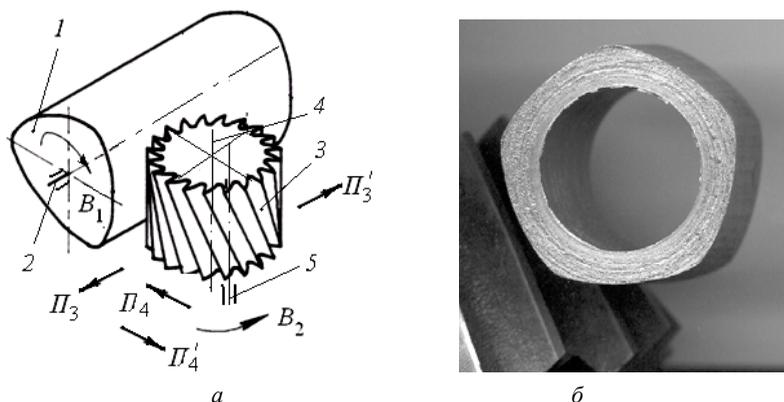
Кинематическая схема обработки некруглой поверхности (а), образец детали с некруглой поверхностью и фрагмент режущей части инструмента (б)
